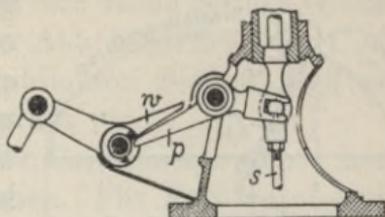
Ventilsteuerung mit Wälzhebeln.
